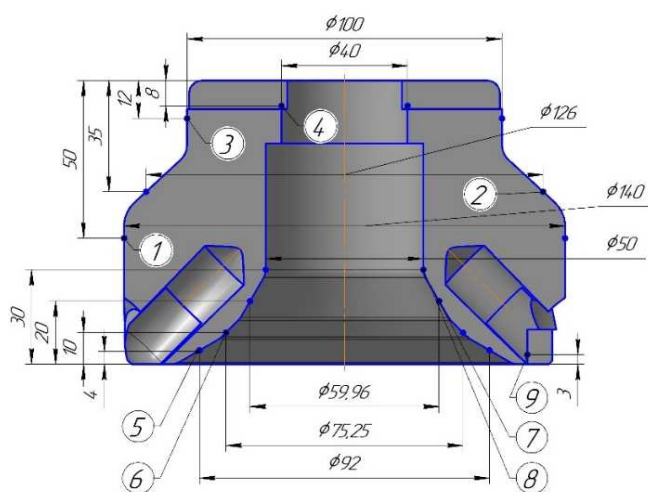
Схема наглядного представления изменений в процесс нагрева корпуса фрезы
